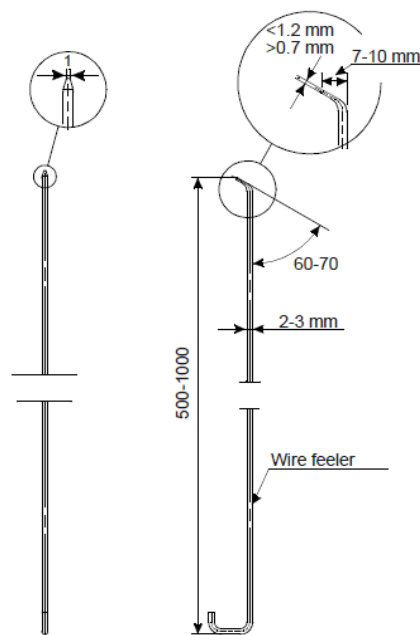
Вимірювання кромки підшипника щупом – проволкою
